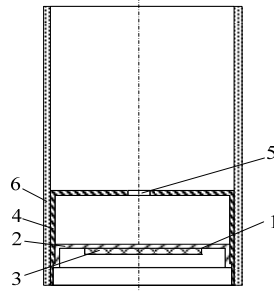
Конструкція ЕАП: 1 – біморфний п'єзоелемент; 2 – металева мембрана; 3 – п'єзоелемент; 4 – корпус перетворювача; 5 – отвір; 6 – порожнистий циліндр
